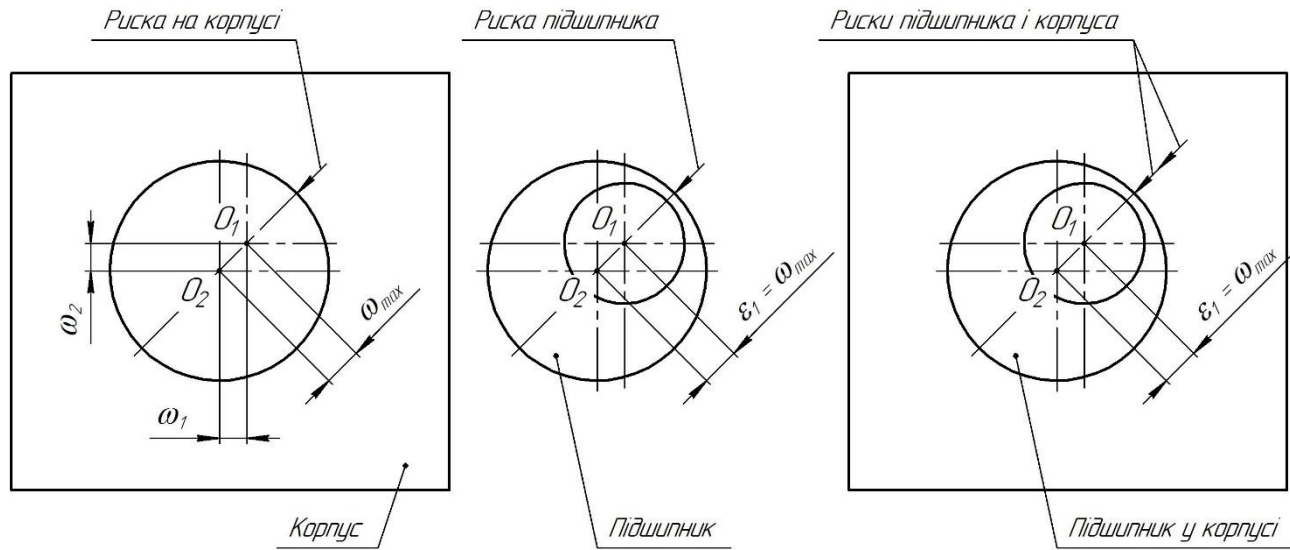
Зменшення похибки повертання осі обертання вала щодо основних баз корпусу
